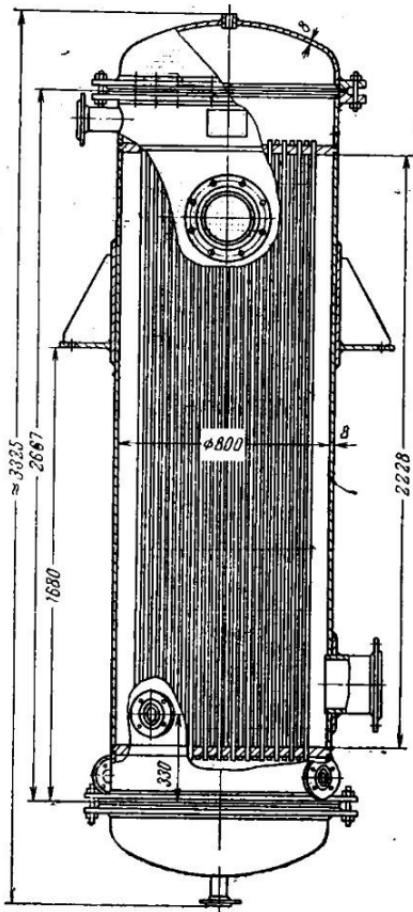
Вертикальный одноходовой дефлектионатор с неподвижными трубными решетками.
